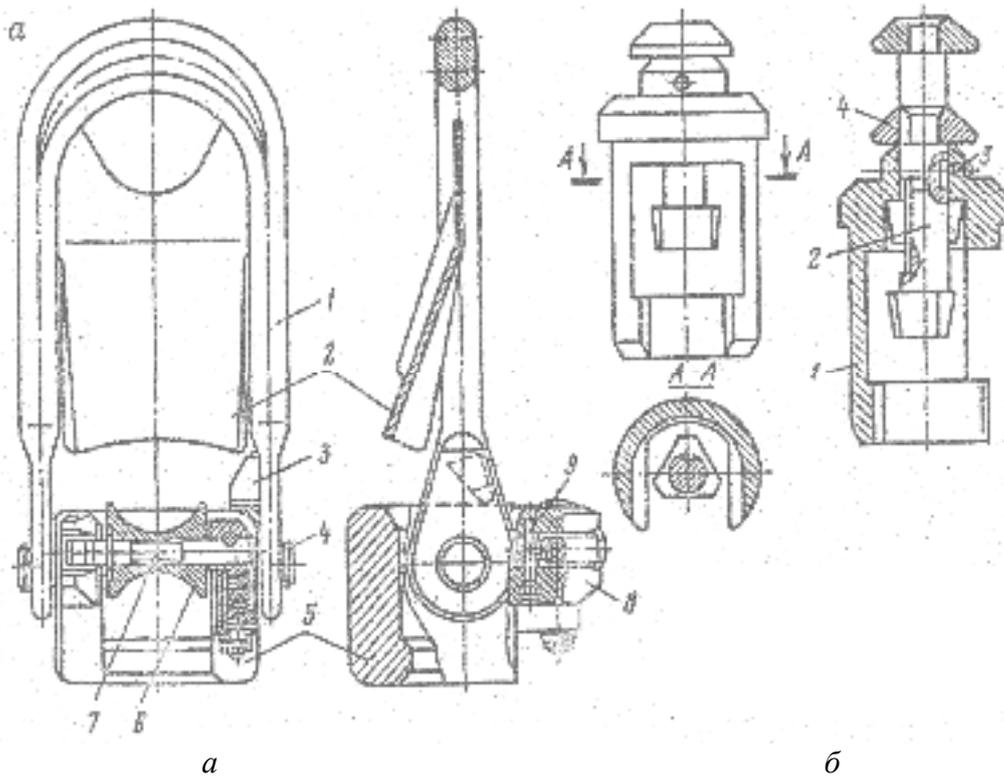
Элеватор МЗ-50-80: 1 – серьга; 2 – корпус; 3 – гайка; 4 – шайба; 5 – втулка; 6 – пружина; 7 – шплинт; 8 – скоба
